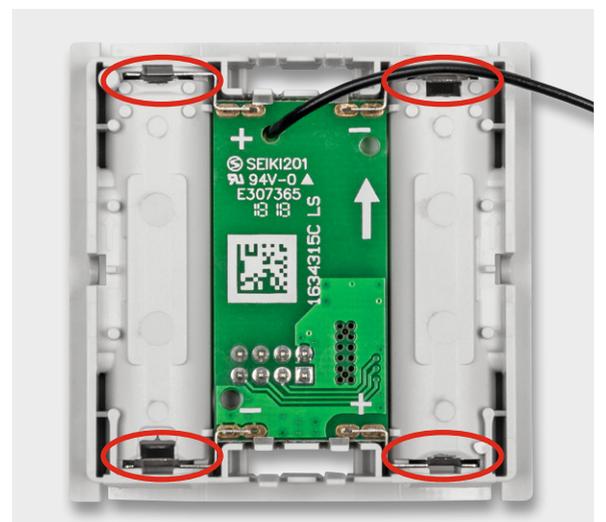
So wird die komplett bestückte Funkplatine eingelegt, die markierten Platinenhalter müssen einrasten.
